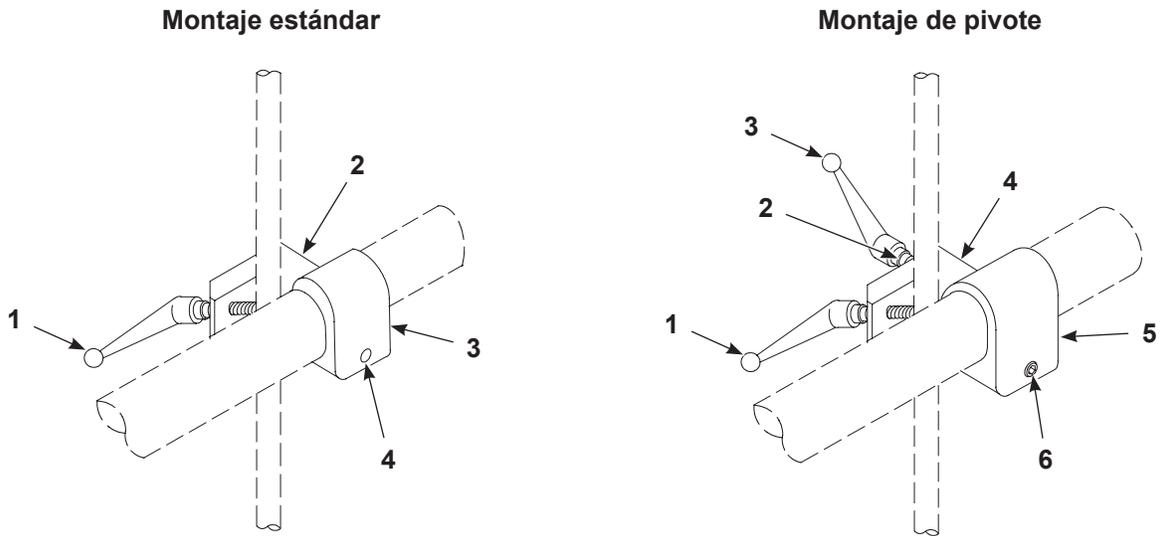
Montajes en barra de pistola de aplicación para pistolas de aplicación de montaje en tubo
